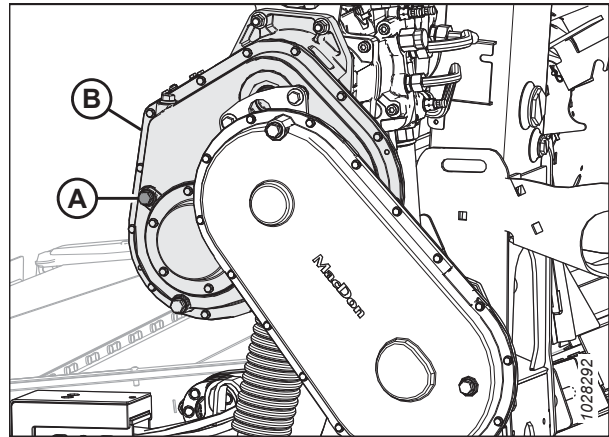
Schneidwerk-Hauptgetriebe
